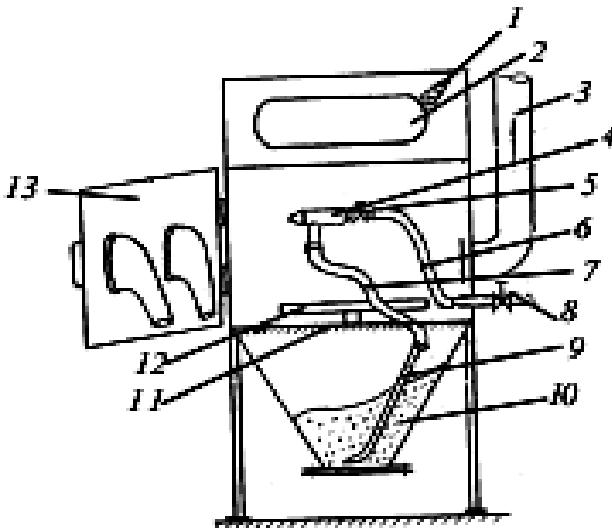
Схема установки струменево-абразивної обробки.
